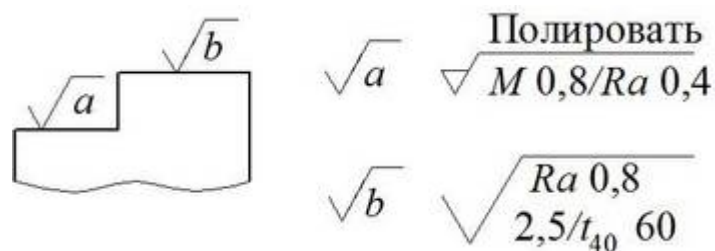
Схема упрощенного обозначения шероховатости поверхностей
